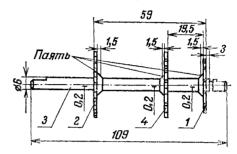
Ротор барабана: 1-2 — диски крепления; 3 — ось (сталь 3); 4 — диск фиксатора.
